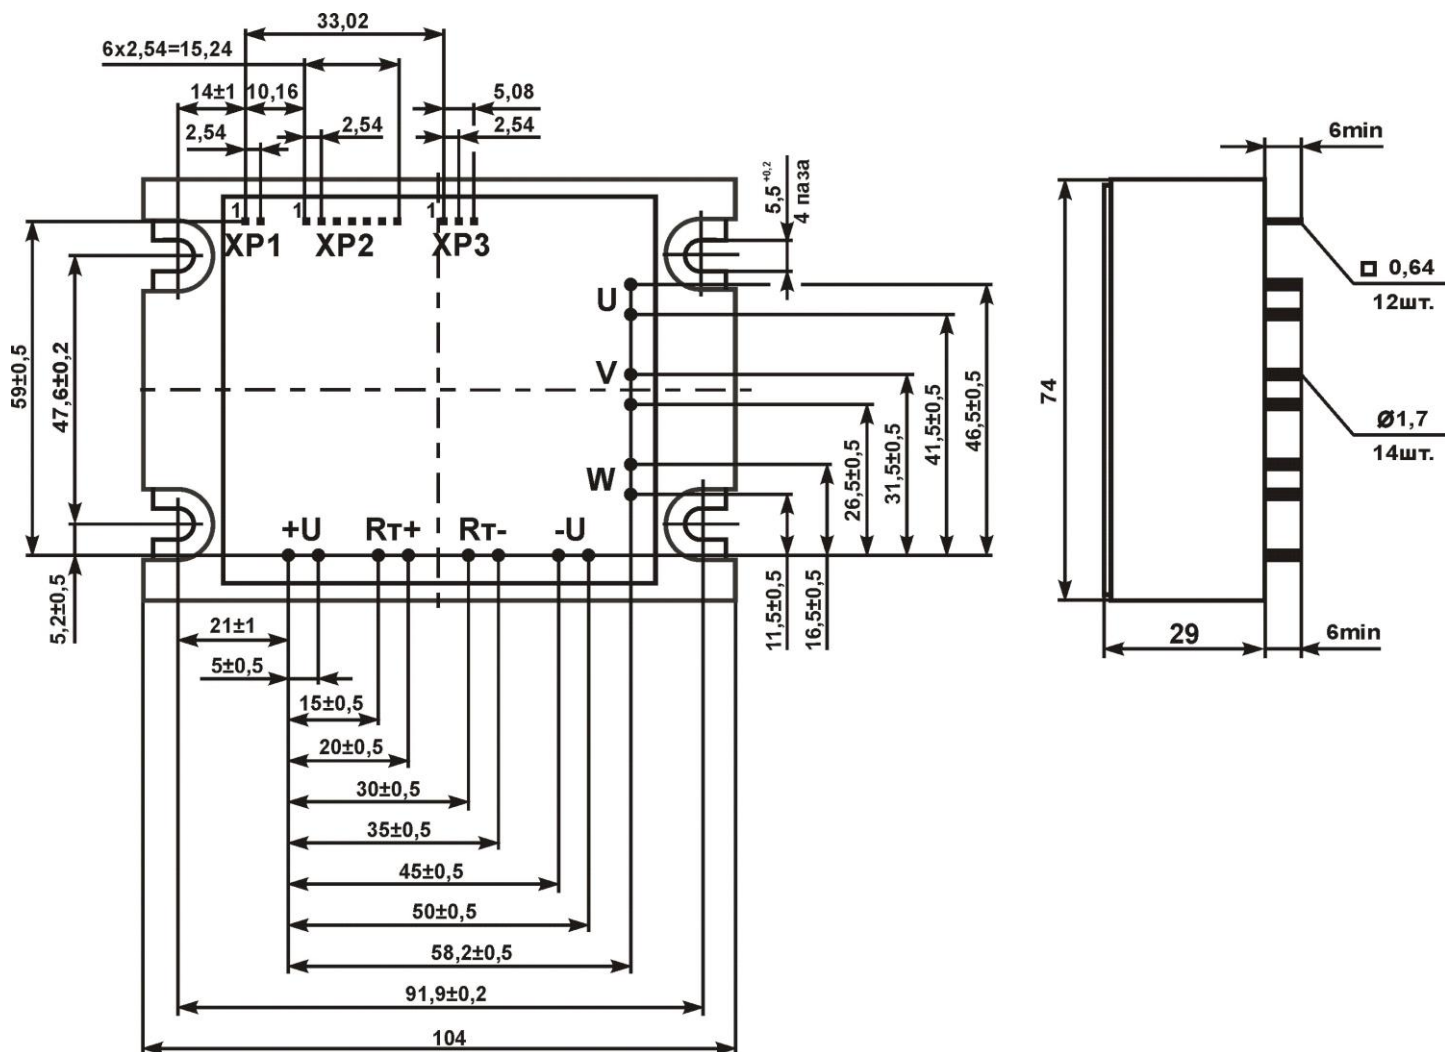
Габаритный чертёж и присоединительные размеры модуля
